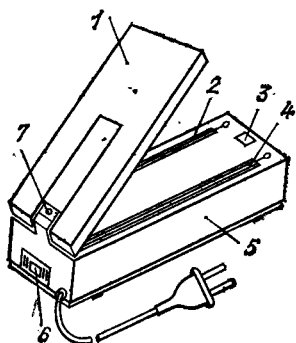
Прибор для сваривания полиэтиленовой пленки «Молния-3»
